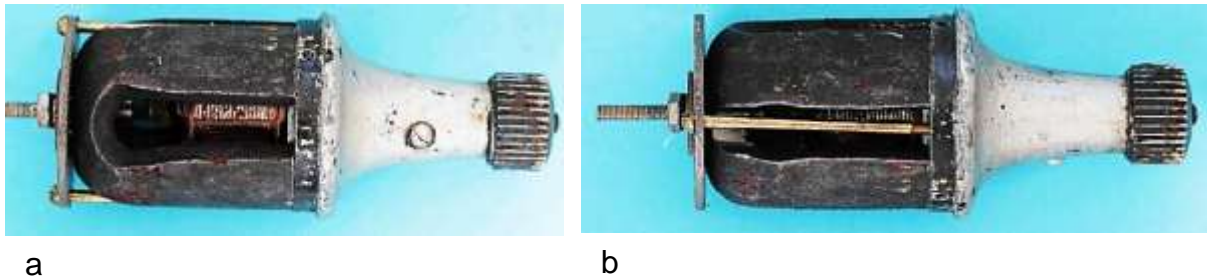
Befestigung des Magneten am Lagerhals: a) Freie Pollücke, b) Pollücke mit Gewindebolzen
